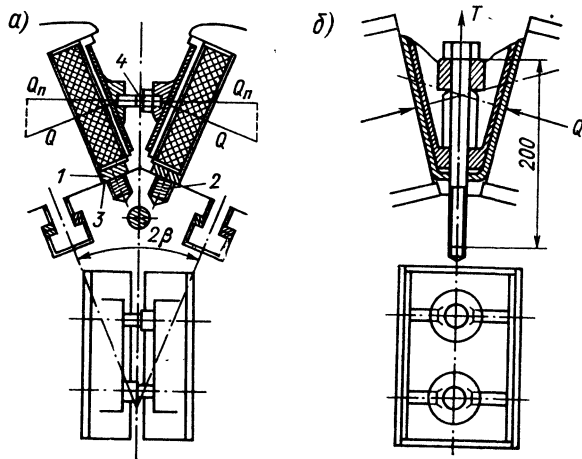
Крепление междуполюсных распорок: а — распорка, расклиниваемая винтовыми шпильками; б — распорка, притянутая болтами к сердечнику ротора
